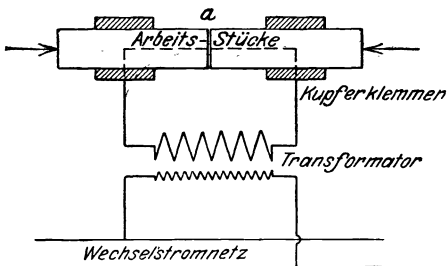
Schema der elektrischen Stumpfschweißung.
